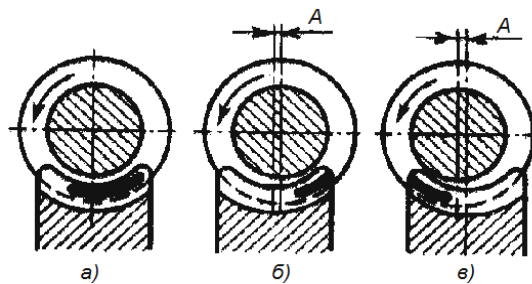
Контроль расположения осей отверстий корпуса червячного редуктора выполнением проверок
